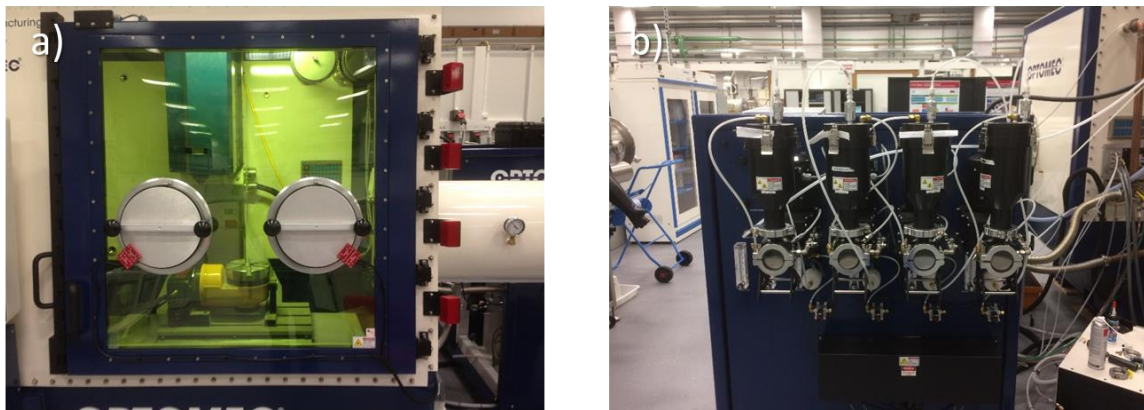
a) Machine Optomec MR-7, b) 4 distributeurs de poudre
